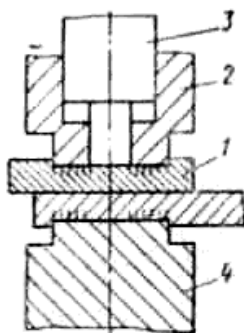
Схема сварки с односторонним деформированием свариваемых деталей: 1 - свариваемые детали, 2 - прижим, 3 - пуансон, 4 - основание.
